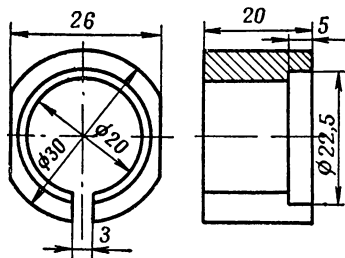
Приспособление для разборки и сборки узла диафрагмы клапана-ограничителя падения давления
